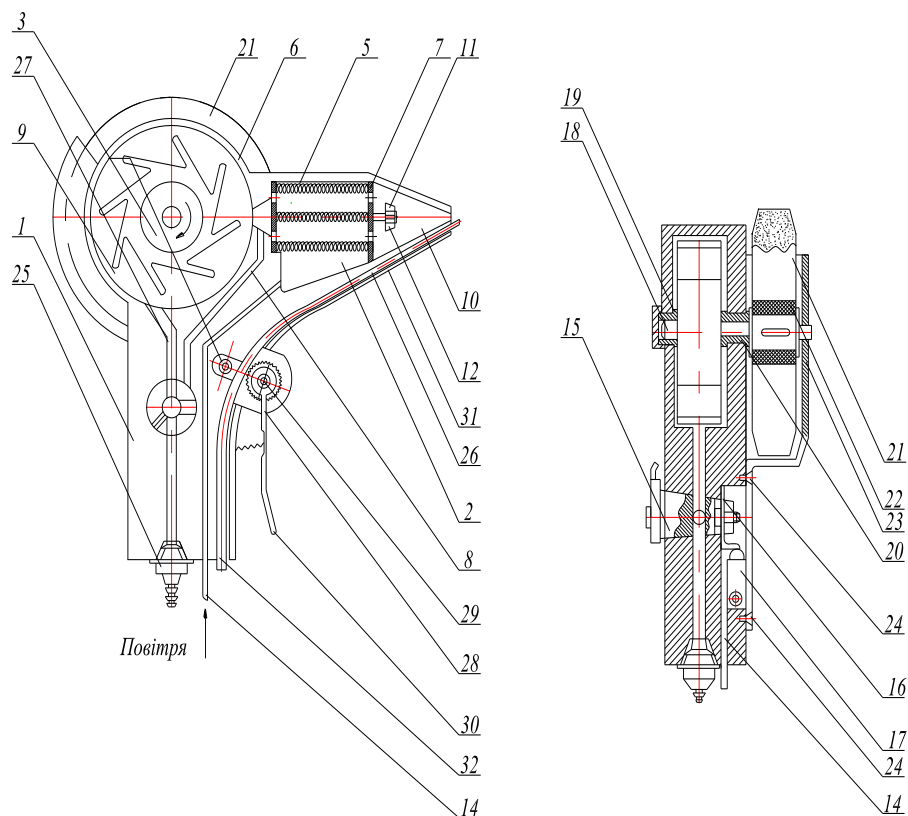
Пристрій для зварювання полімерних матеріалів
